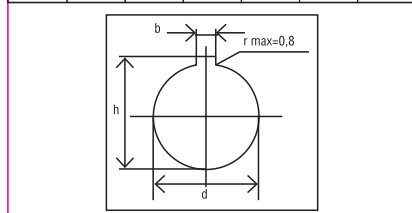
Габаритные и установочные размеры устройств PE-22-BL
